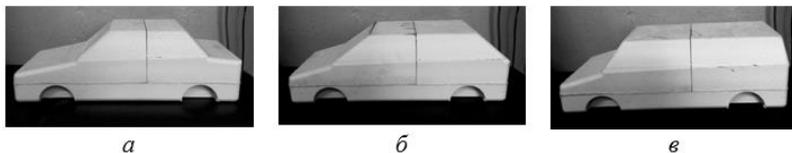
Вид моделей автомобиля после обработке на фрезерном станке с ЧПУ
